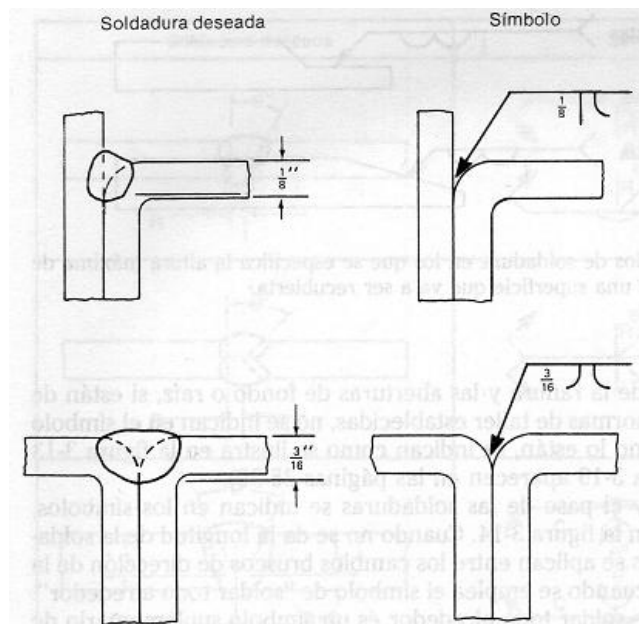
Símbolo de soldadura en los que se especifica el tamaño de las soldaduras de ranura con acampanado.
